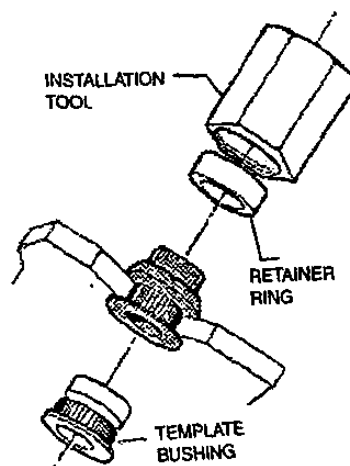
Los casquillos de plantilla se instalan con una herramienta de instalación.
